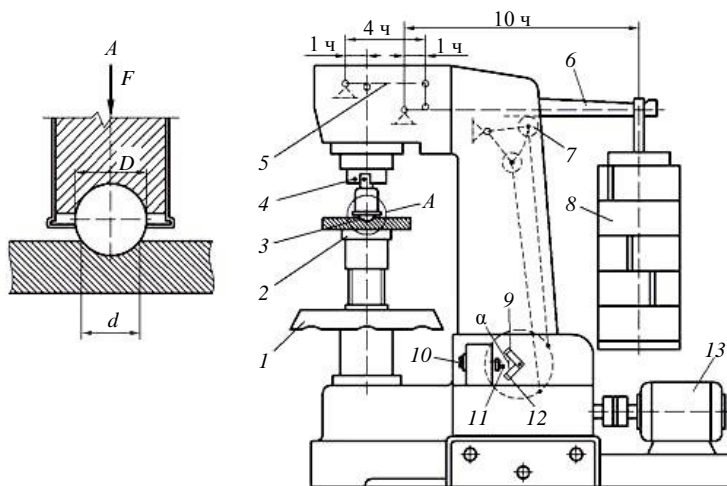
Схема твердомера ТШ-2: 1 – маховичок; 2 – предметный столик; 3 – шарик; 4 – шпindel; 5, 6 – рычаг; 7 – подвижная опора; 8 – грузы; 9, 12 – кулачки; 10 – кнопка пуска; 11 – концевой переключатель; 13 – электродвигатель
